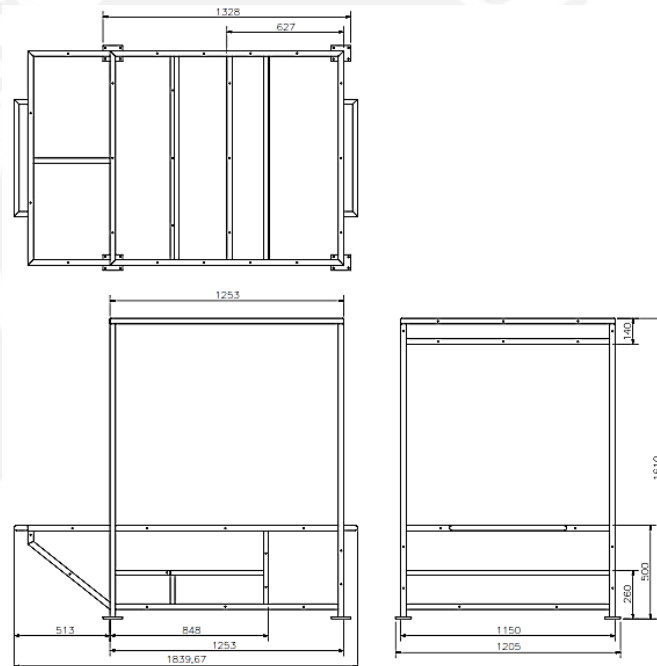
Estructura de perfiles – Plano PD1.1.2-A3
